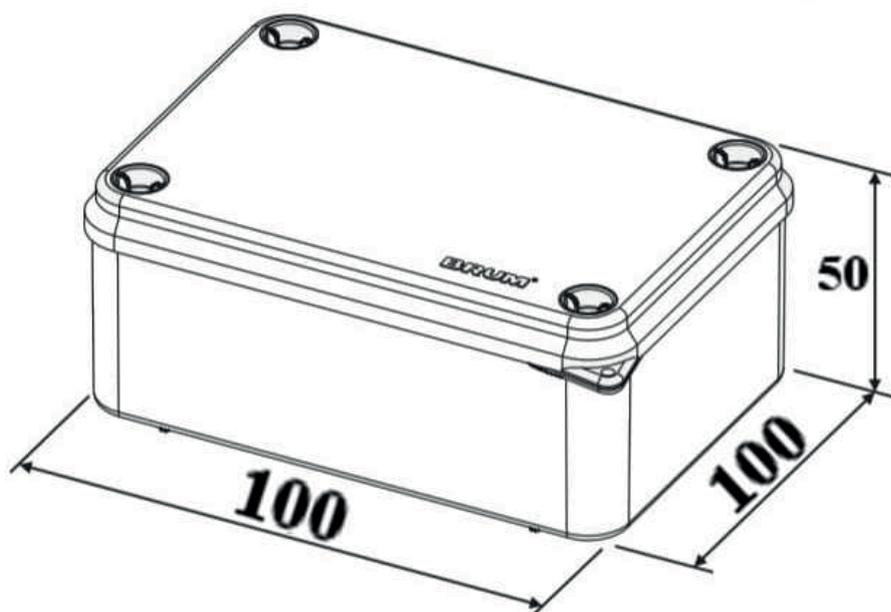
DIMENSÕES DA CAIXA DE PASSAGEM (MM)
